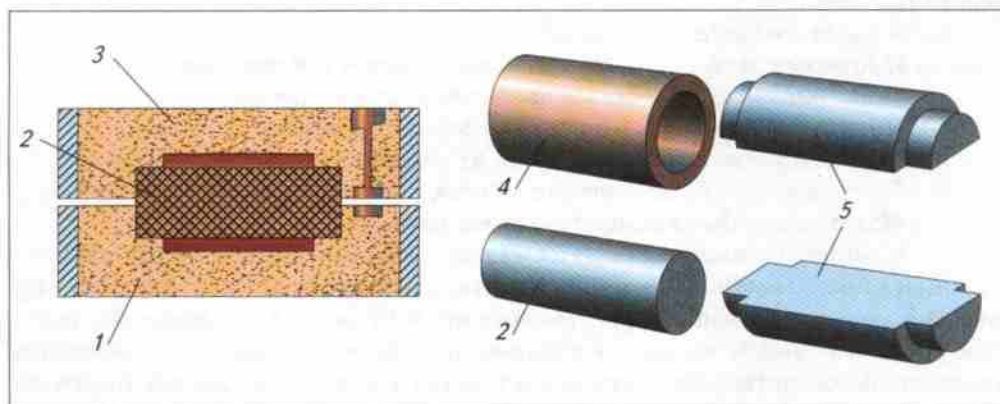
Литейная форма: 1 — нижняя опока; 2 — стержень; 3 — верхняя опока; 4 — отливка; 5 — модель
